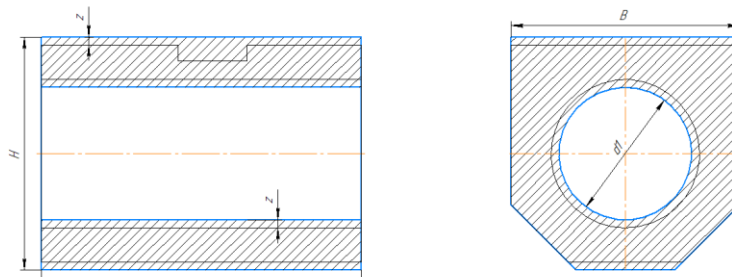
Ескіз деталі корпус з контуром заготовки
